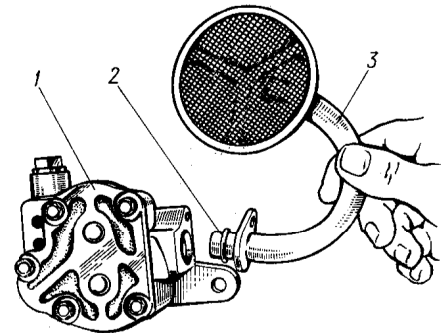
Снятие маслоприемника и уплотнительного резинового кольца:
